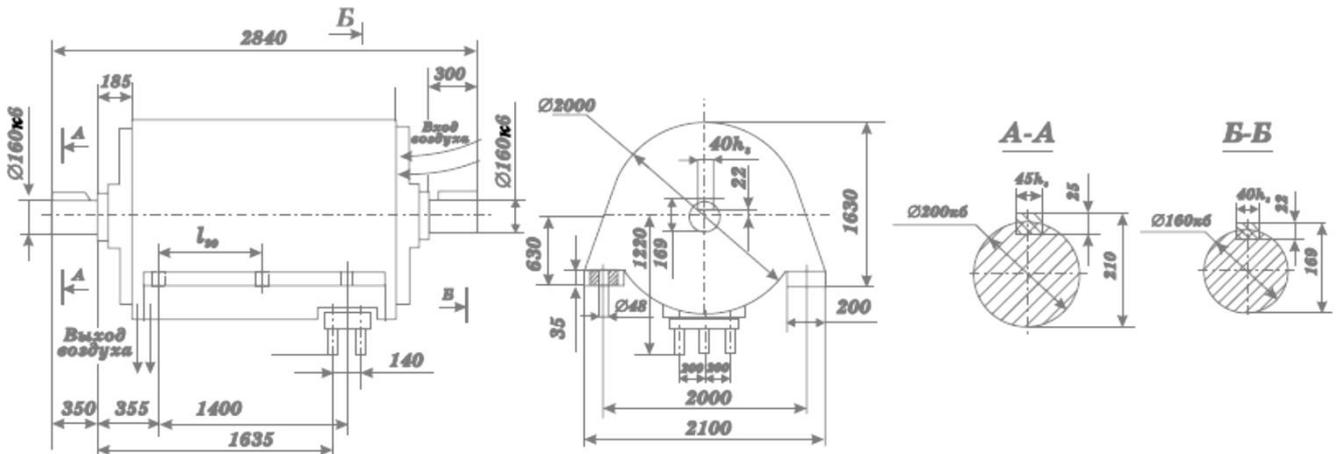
Габаритные, установочные размеры двигателей СДЭ2 17-го габарита с частотой вращения 750 об/мин.
